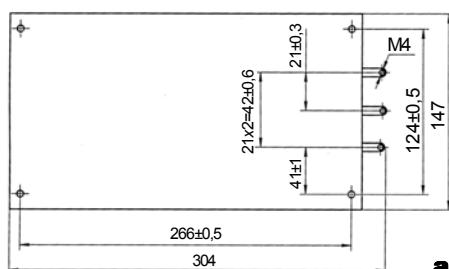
Габаритные, установочные и присоединительные размеры блоков конденсаторов типа БК-403.
